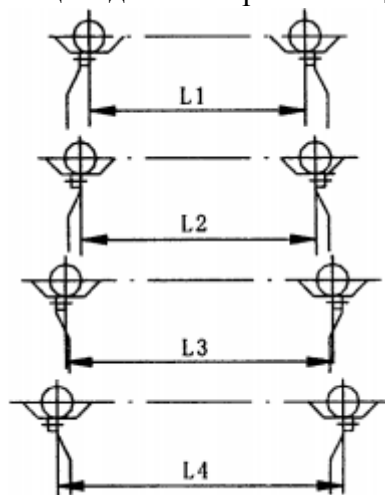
Рисунок регулировки колеизадних колёс
